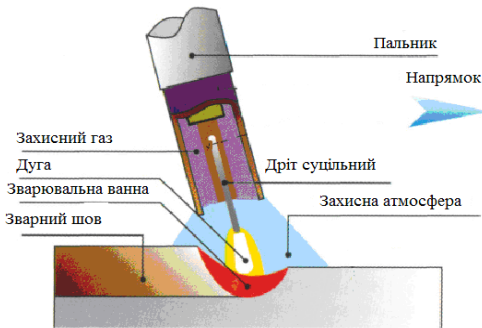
Схема зварювання у і низьколеговану сталі.
